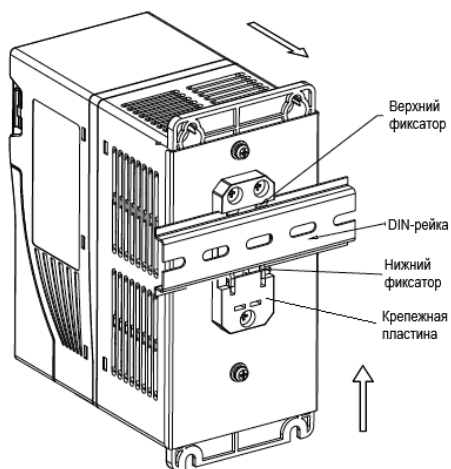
Установка преобразователя на DIN-рейку
